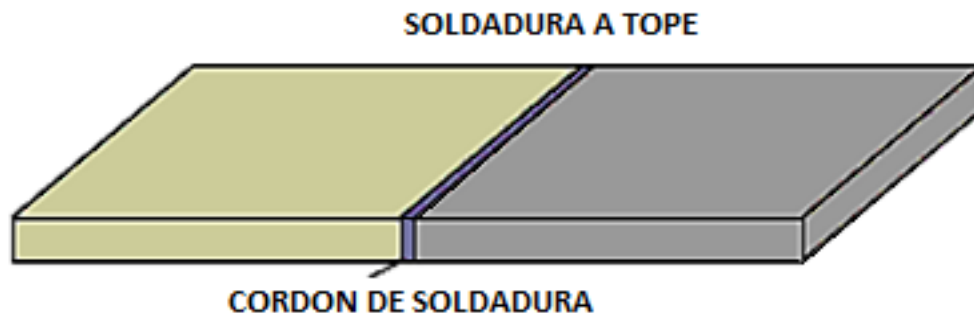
Esquema representativo de soldadura a tope.
